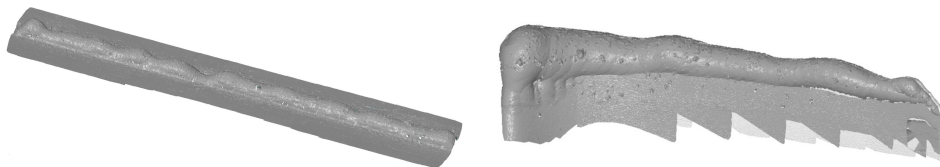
Schweißnaht auf Flachprobe; Reparaturschweißnaht an Turbinenschaufeltyp
